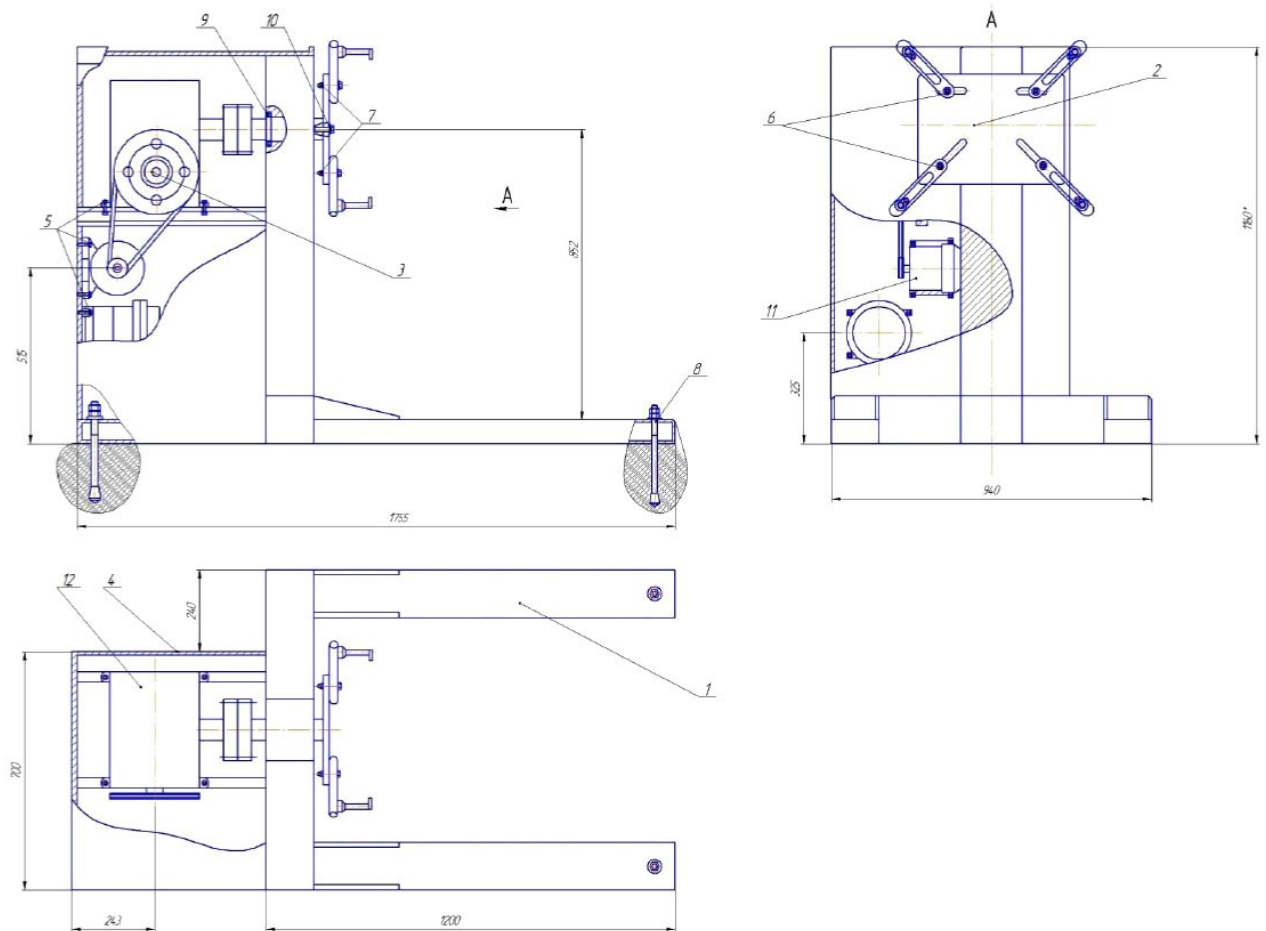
Загальний вид стану: 1 – підстава; 2 – магнітний пускач; 3 – електродвигун; 4 – клинопасова передача; 5 – черв'ячний редуктор; 6 – фланцева муфта; 7 – вихідний вал стану; 8 – каркас; 9 – шпindel; 10 – кронштейн; 11 – проміжна опора.
